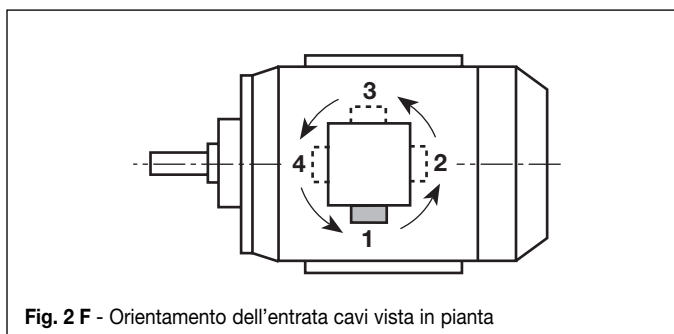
F - Orientamento dell'entrata cavi vista in pianta
